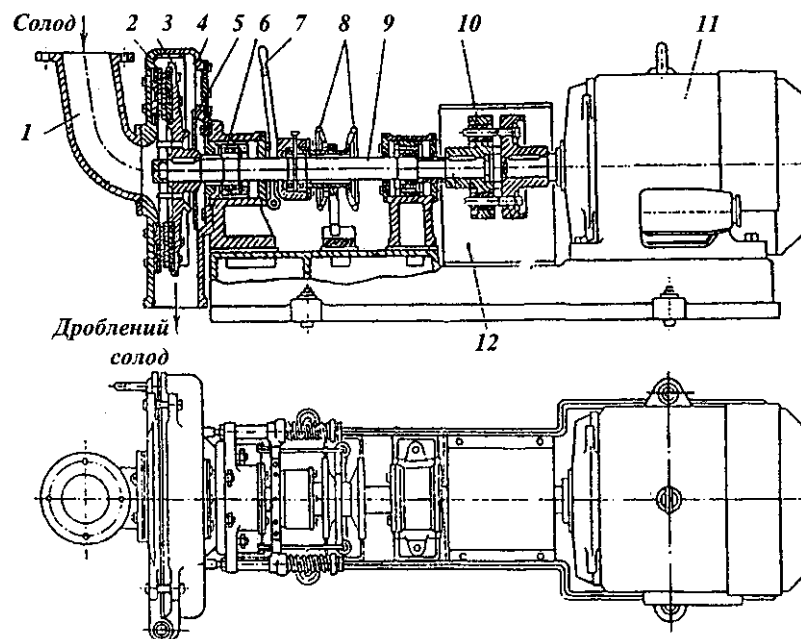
Дробарка дискова: 1 – патрубок живильний; 2 - кришка рухома; 3 - диск; 4 - корпус;
